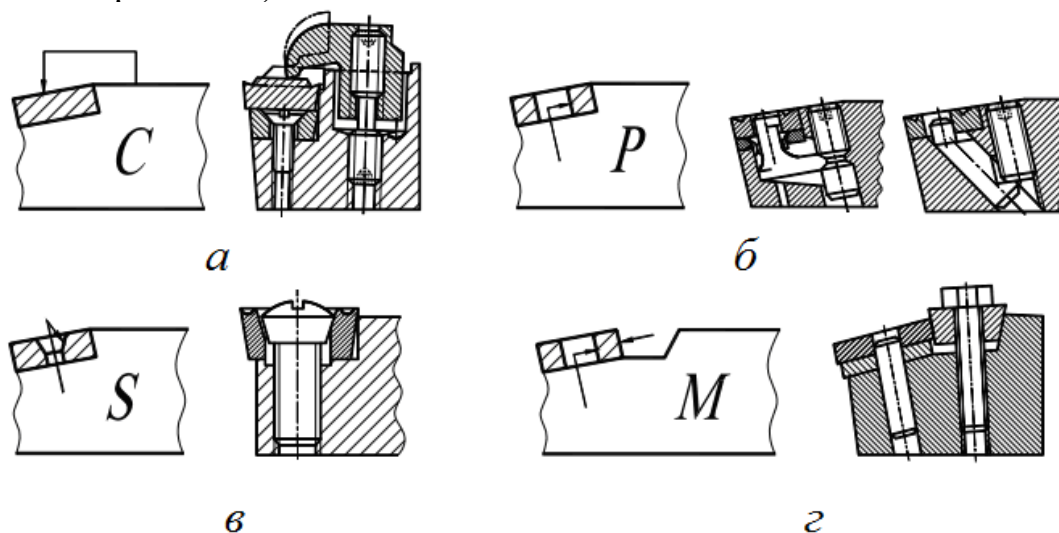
Условные обозначения способов и схемы конструкций устройств механического крепления СМП на державке резца (корпусе инструмента)
